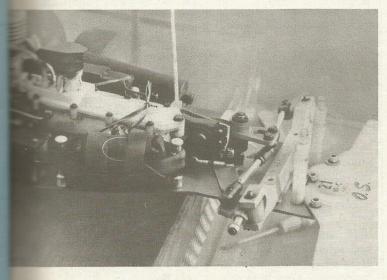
Die Vorderachse ist als Pendelachse ausgelegt. Sie wird auf einer separaten GFP-Platte (3 mm) zusammen mit dem Servoschützer und dem Lenkservo montiert. Diese Platte wird mit dem anderen Chassisteil durch Schrauben, die in Gummiformstücken geführt sind, verbunden. Durch die Schrauben läßt sich die Pendelwirkung einstellen
